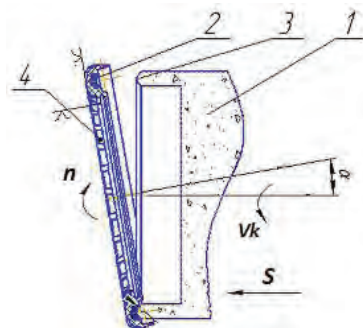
Схема лобового шлифования дорожек качения колец упорных подшипников
